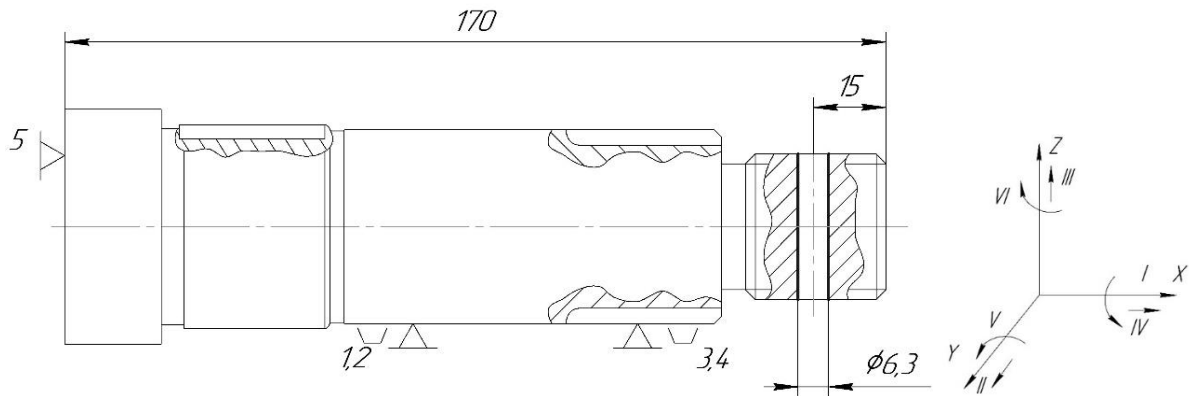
Схема базування і закріплення заготовки при операції
